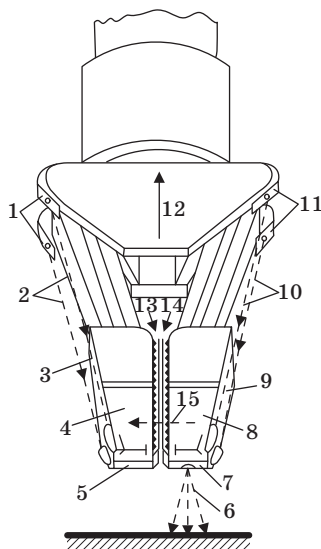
Внешний вид схвата, оснащенного датчиками
